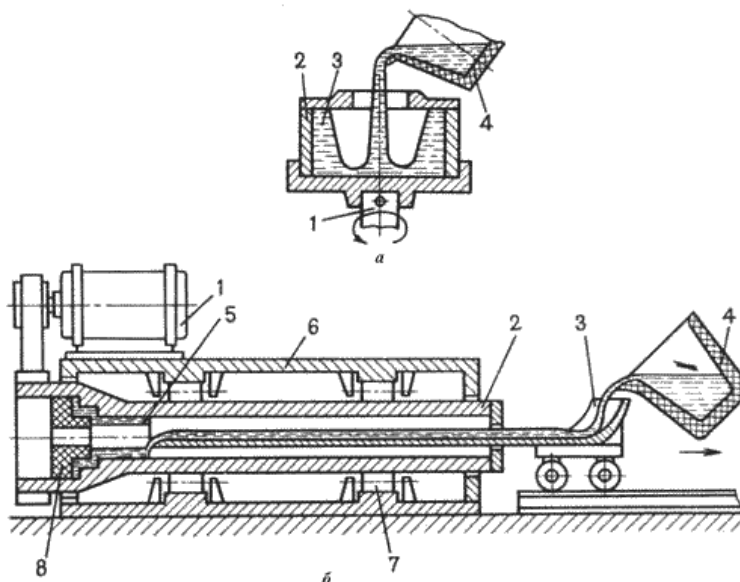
Схемы процессов изготовления отливок центробежным литьем
